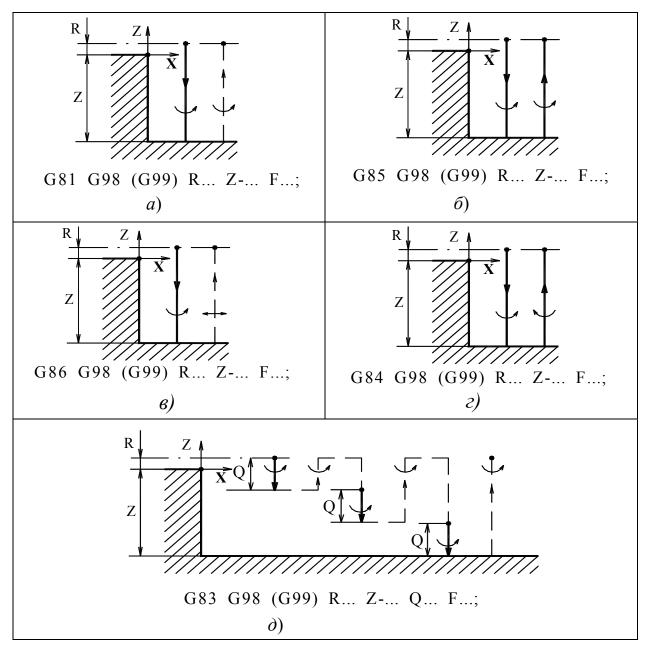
Графическая интерпретация циклов сверления: a — цикл короткого сверления; δ , ϵ — циклы развертывания; ϵ — цикл нарезания резьбы метчиком; δ — цикл ступенчатого сверления
